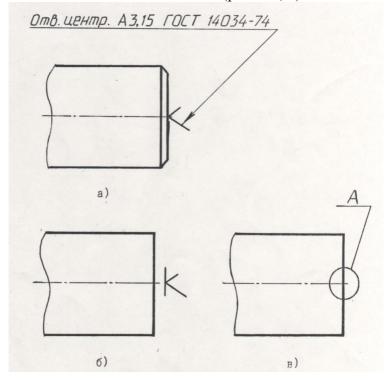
Обозначение центровых отверстий на чертежах.
